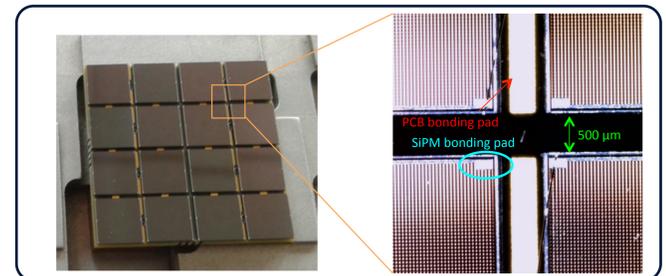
Modulo equipaggiato con 16 sensori NUV-HD assemblati su PCB di supporto con macchina die-bonder.
